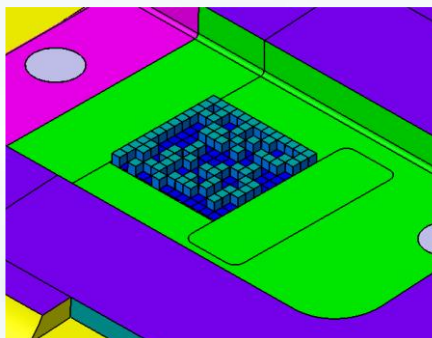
CAD-Modell einer Werkzeugintegrierten individuellen Bauteilmarkierung Foto: Formconsult Werkzeugbau GmbH
